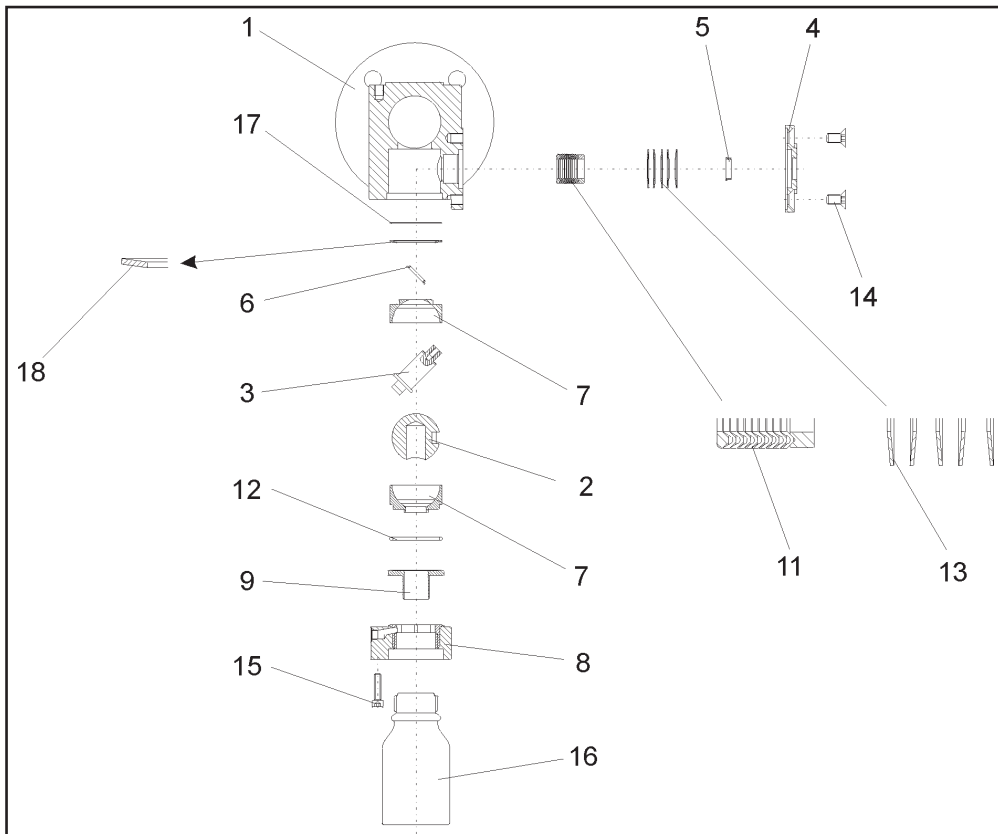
Explosionszeichnung des Probenehmerhahns BR 27a
